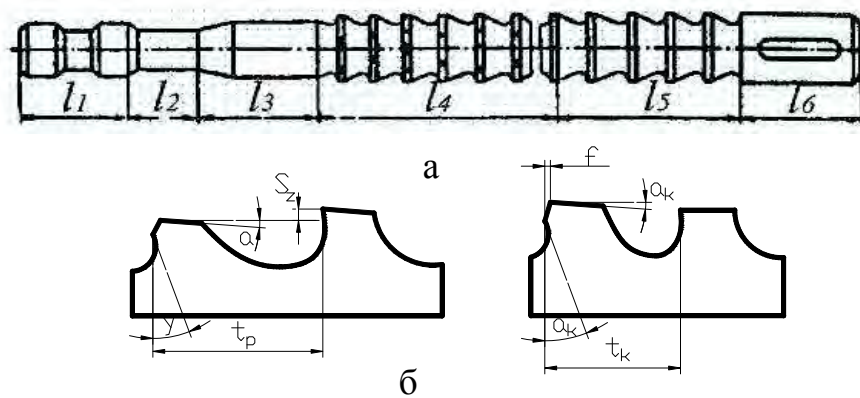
Загальний вид круглої протяжки і геометричні параметри її зубців
